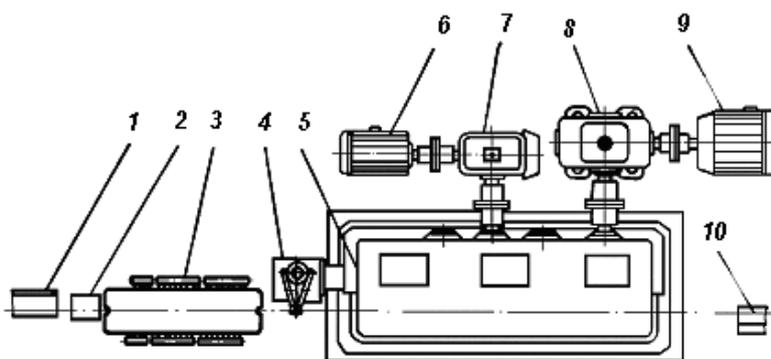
Схема стана для бесконтейнерного вибрационного прессования прутков из тугоплавких металлов
